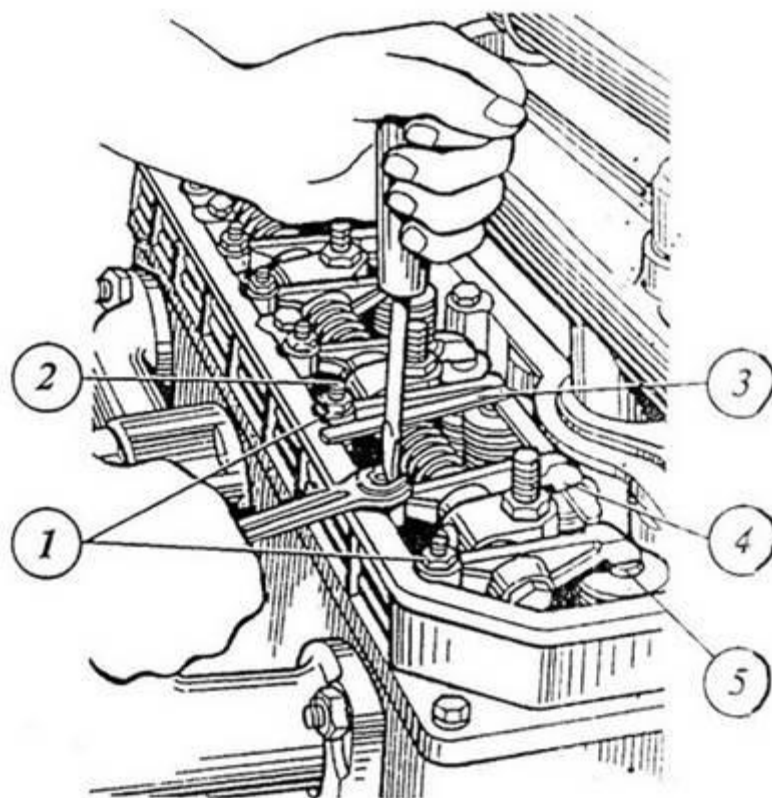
Проверка и регулировка зазоров: 1-контргайка, 2-регулирующий винт, 3-щуп, 4- боек коромысла, 5- стержень клапанов
